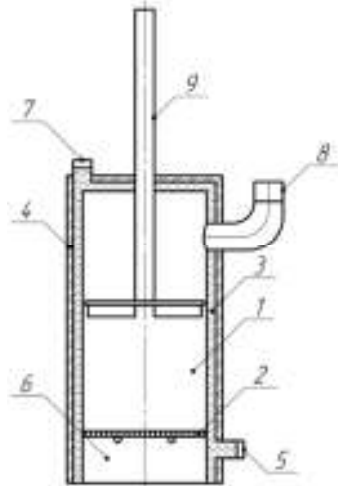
Будова котла прямого горіння: 1 – топка; 2 – колесникова решітка; 3 – водяна рубашка; 4 – корпус котла; 5 – патрубок зворотної подачі; 6 – зольник; 7 – патрубок подачі; 8 – димохід; 9 – труба для подачі повітря
